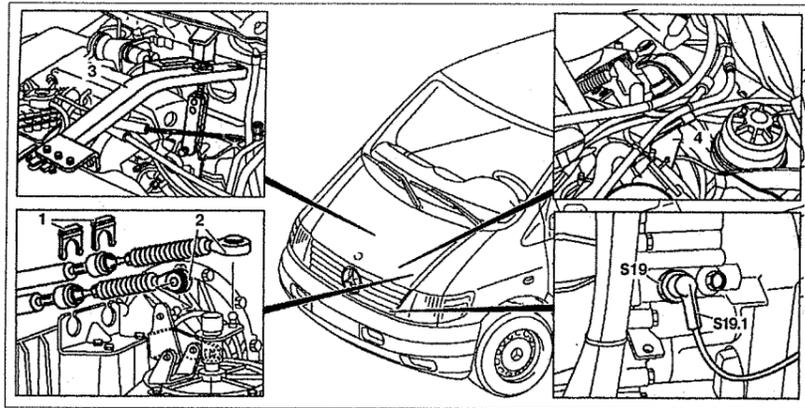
а. Снятие и установка коробки передач (автомобили с двигателями 111.948 и 601.970):
